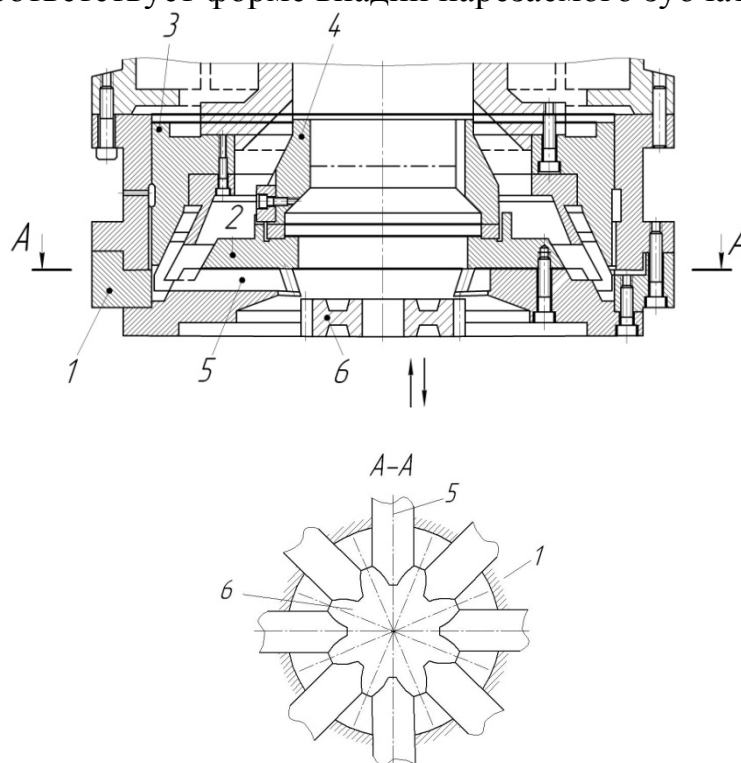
Зубодолбежная головка для нарезания цилиндрических зубчатых колес
